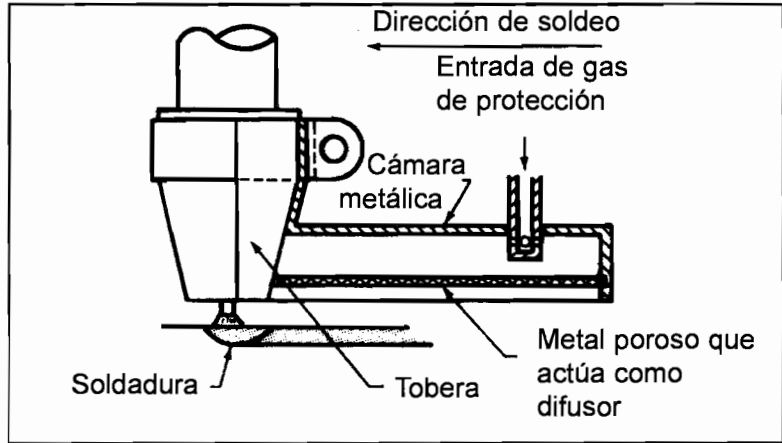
CÁMARA REMOLCADA PARA SOLDEO DE TITANIO
